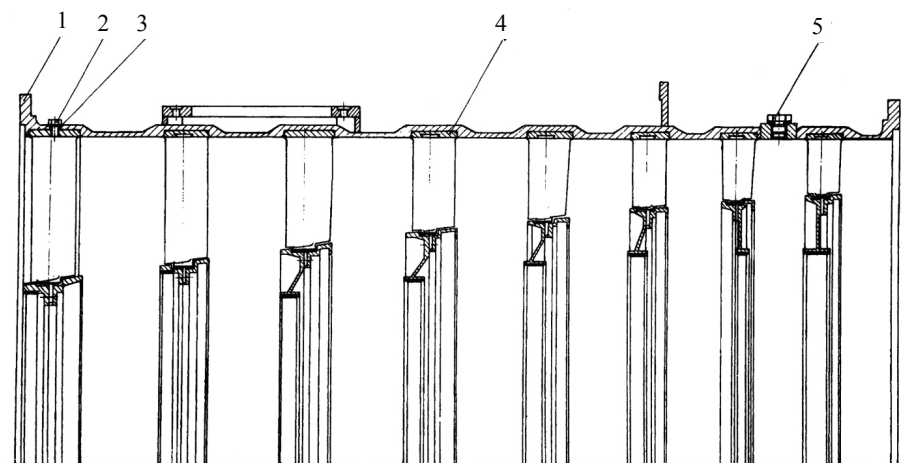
Корпус компрессора низкого давления ДГ90:
